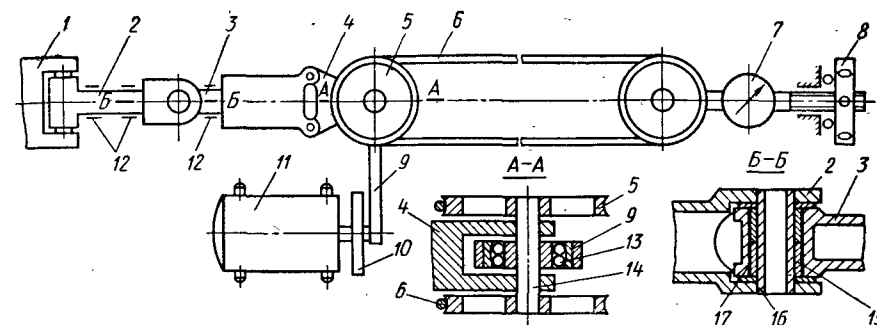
Стенд вертикального шарнира несущего винта вертолета
